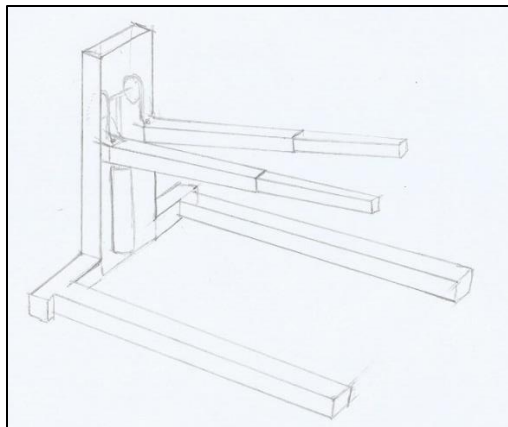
Primer boceto tipo elevador. Fuente: Elaboración Propia.
